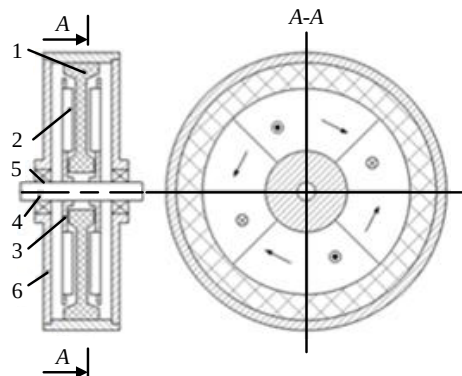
Двухсторонняя дисковая машина без магнитопроводов на статоре и роторе: 1 – обмотка беспазового безжелезного статора; 2 – ВПМ; 3 – двойной ротор; 4 – вал; 5 – подшипники; 6 – корпус
